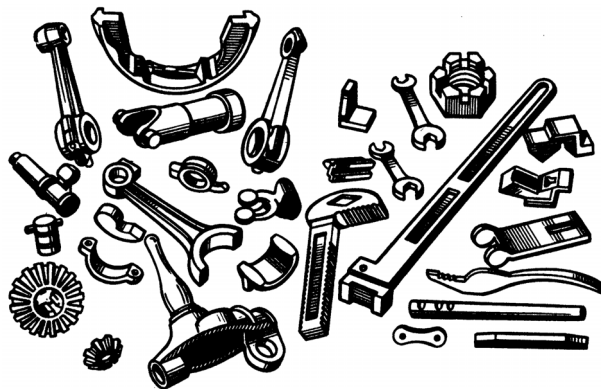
Заготовки, обрабатываемые наружным протягиванием
